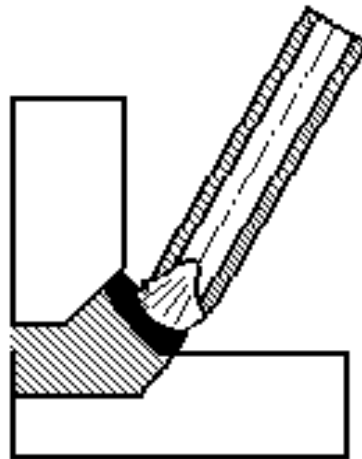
Схема зварювання методом спирання кутового зварного шва
